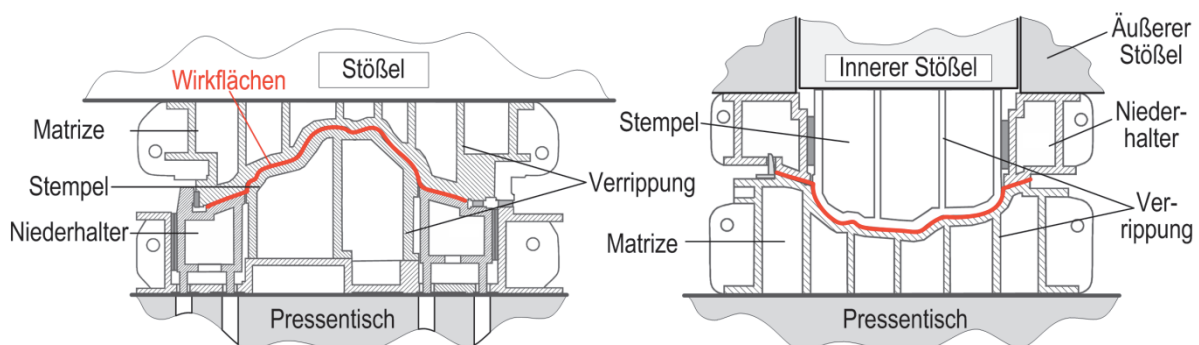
Prinzipieller Aufbau von Tiefziehwerkzeugen (in Anlehnung an [9]); links Werkzeug für einfachwirkende Presse; rechts: Werkzeug für doppeltwirkende Presse
